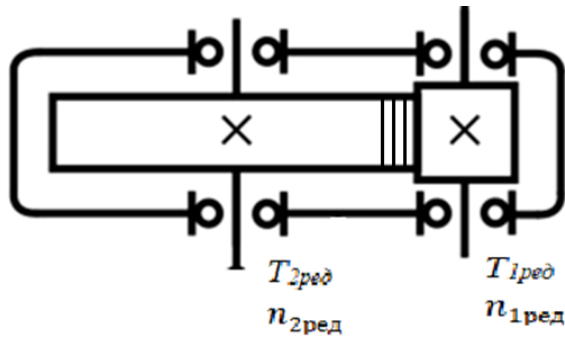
Кінематична схема редуктора циліндричного прямозубого одноступеневого
